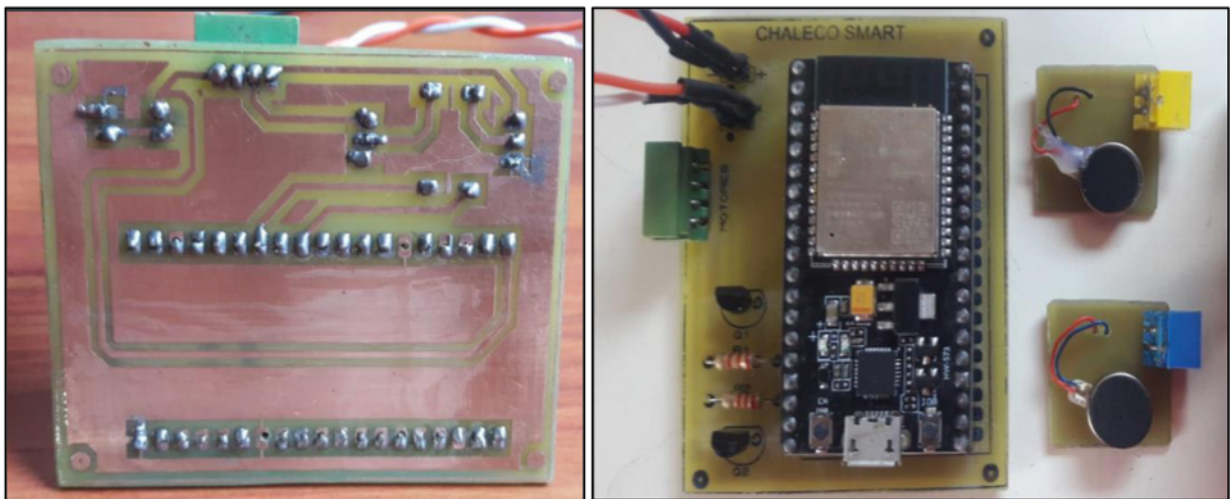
Montaje y soldadura de los elementos en la placa
